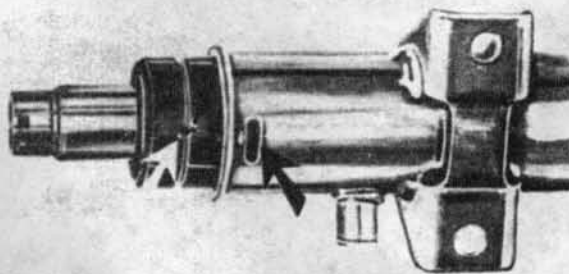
Взаимное положение уплотнительной втулки и отверстия в корпусе перед установкой предохранительной (блокирующей) проволоки
